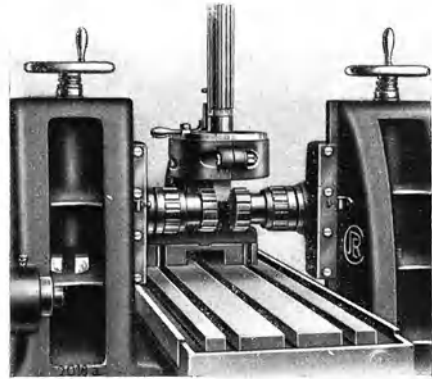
Die Doppelfräsmaschine von J. E. Reinecker.
